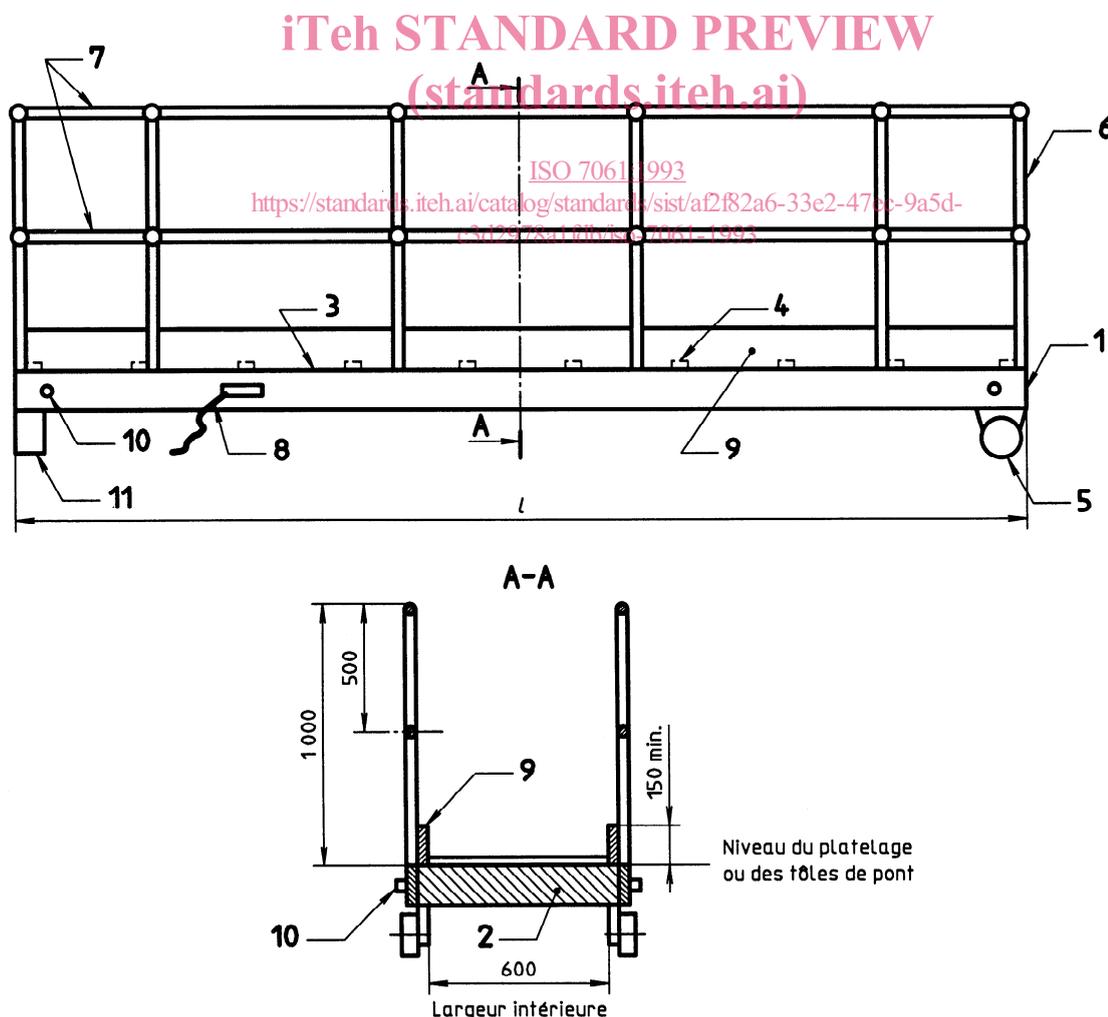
Disposition générale d'un planchon (voir le tableau 1 pour la nomenclature)
